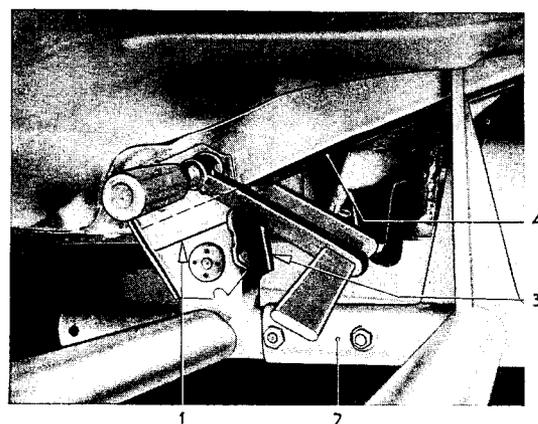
Neue Hinterfederstützen zum Hinterlängsträger ausgerichtet
